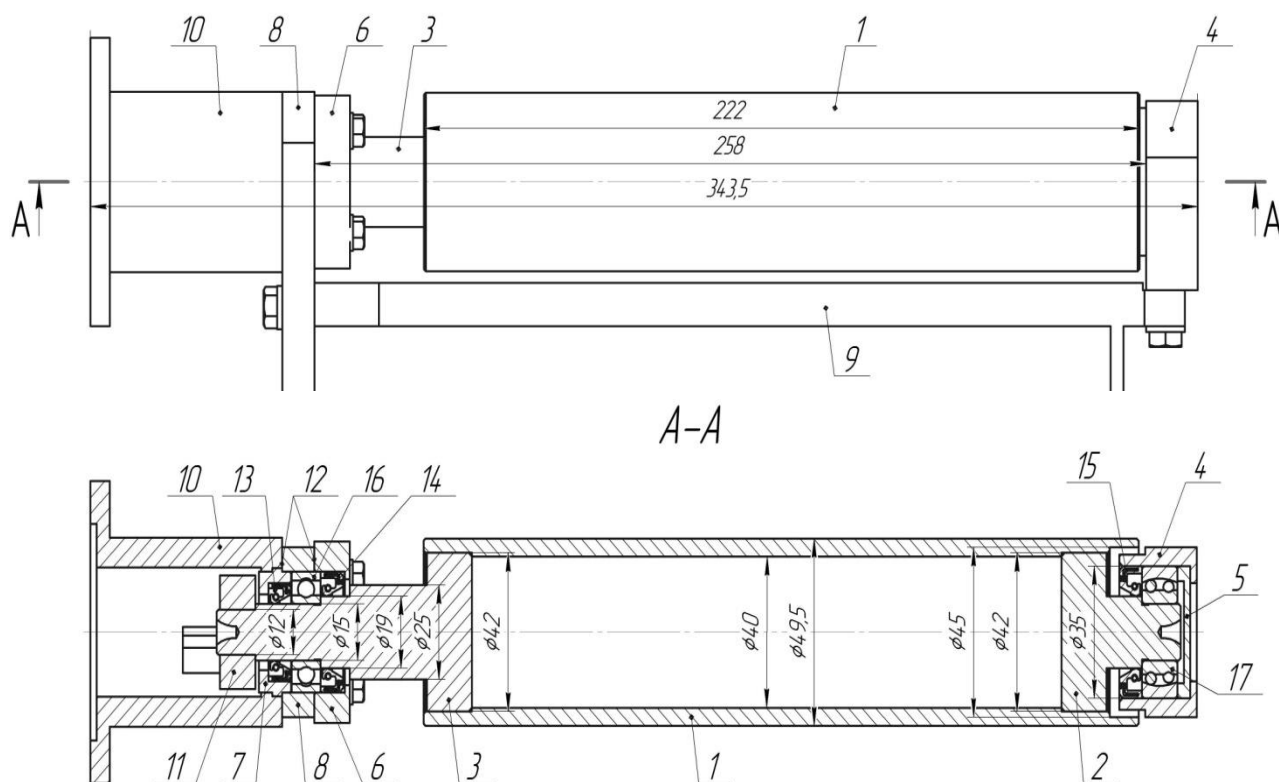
Сборочный чертеж модернизированного ведущего узла:
